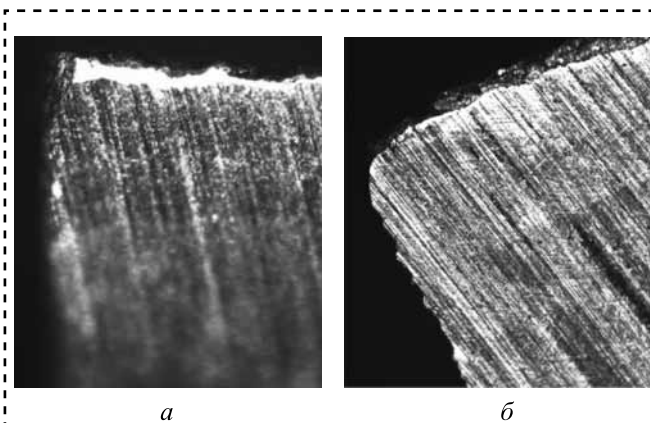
Внешний вид износа резца по задней поверхности (опыт № 12): а — до испытаний; б — после испытаний
